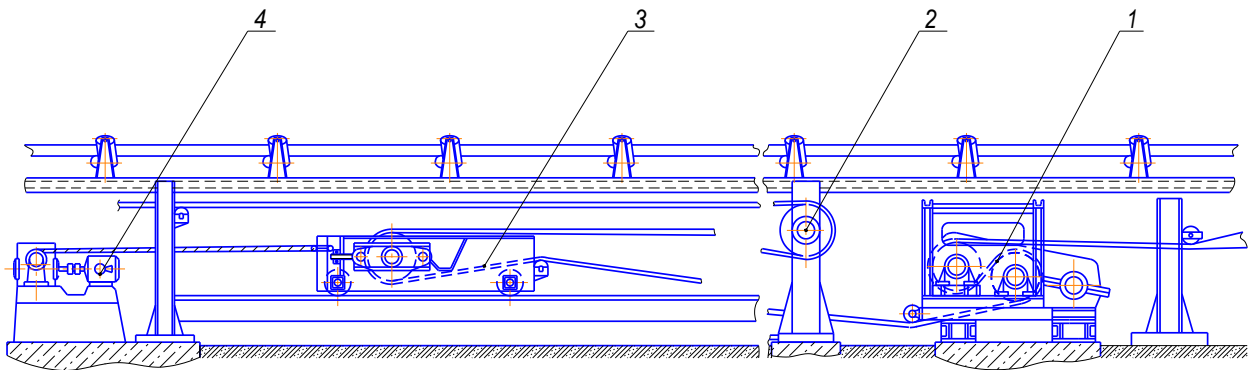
Привід із натяжним телескопічним пристроєм: 1 – привід стрічкового конвеєра; 2 – нерухомий барабан телескопічного пристрою; 3 – рухлива каретка телескопа; 4 – натяжна лебідка телескопічного пристрою
